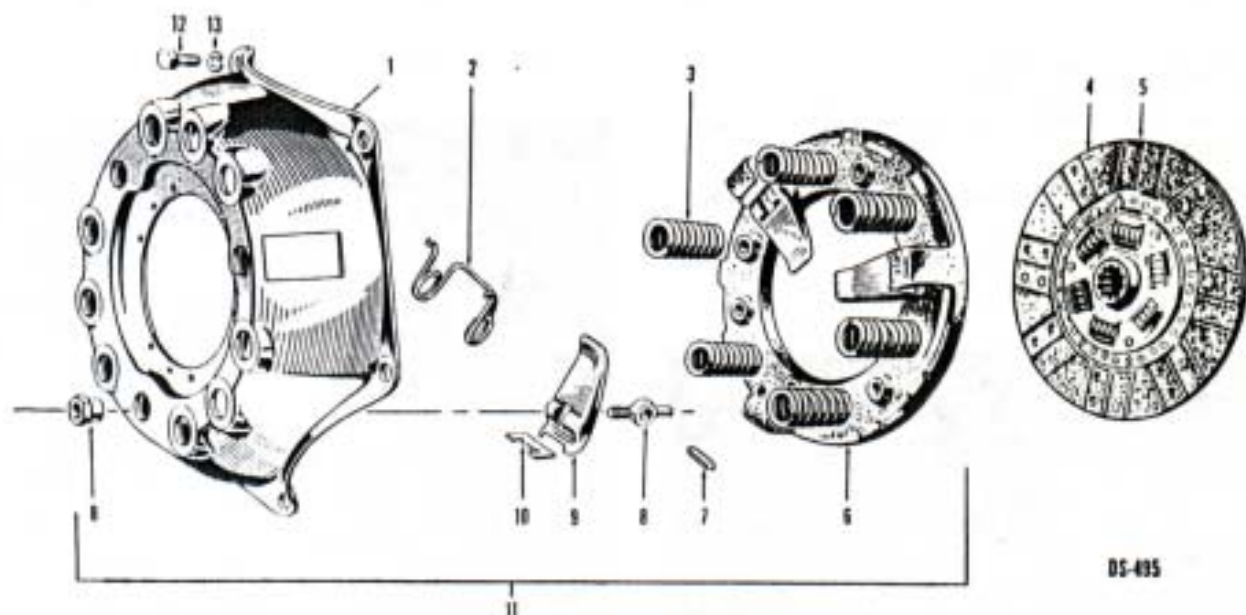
Conjunto del embrague "WOBRON" (Borg y Beck 1304).
